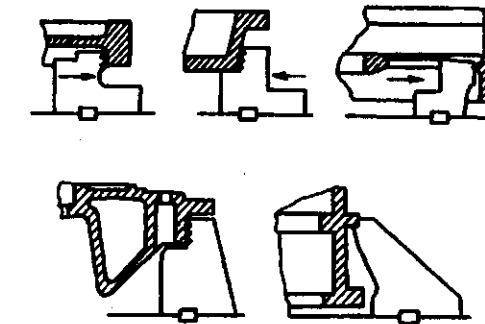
Схемы закрепления заготовок на планшайбе станка
